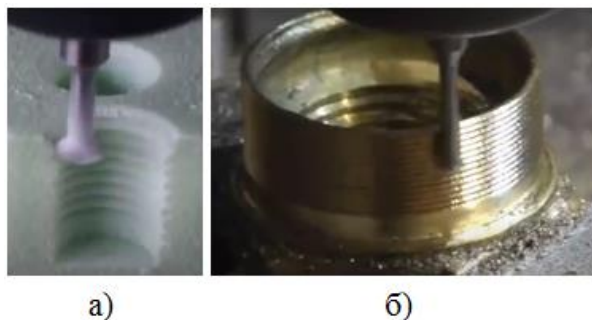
Нарізування різьби одновитковою різьбофрезой: а) внутрішньої; б) зовнішньої
